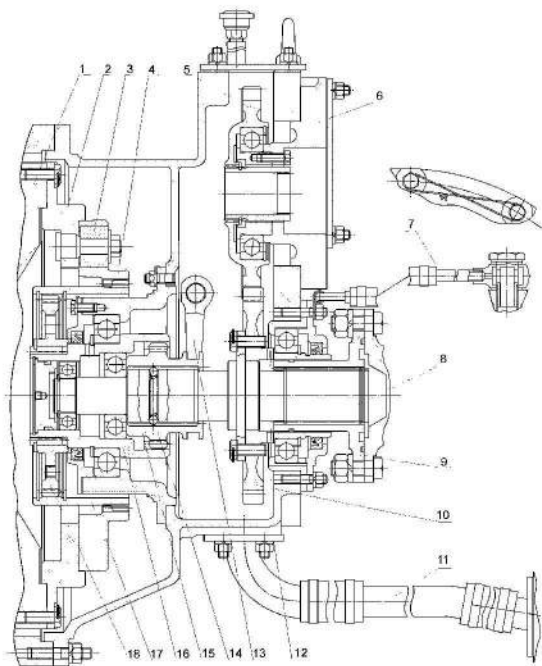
Редуктор с полужесткой муфтой: 1 – маховик двигателя; 2 – диск; 3 – резиновая втулка; 4 – муфта; 5 – ведомая шестерня привода насоса; 6 – стакан; 7 – трубопровод; 8 – ведущий вал редуктора; 9 – фланец; 10 – ведущая шестерня привода насосов; 11 – трубопровод слива масла; 12 – поворотный уголок; 13 – вилка отключения двигателя; 14 – фиксатор; 15 – муфта отключения двигателя; 16 – вал-муфта; 17 – муфта наружная; 18 – муфта внутренняя.
